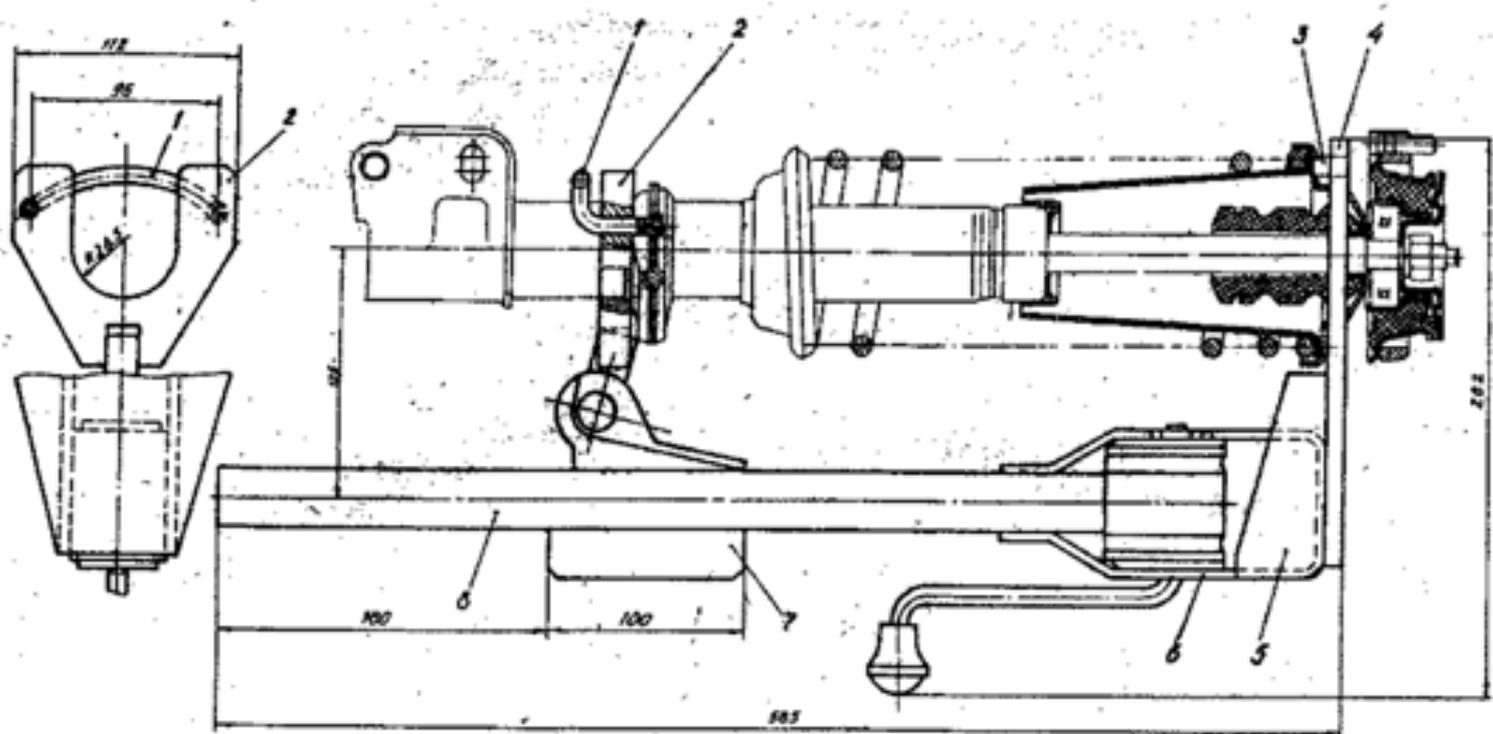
Приспособление М9832-559-01 для сборки и разборки стойки передней подвески (вариант): 1 - скоба; 2 - вилка; 3 - упор; 4 - захват; 5 - косынка; 6 - стремлянка; 7 - фланец; 8 - механизм приводной.
